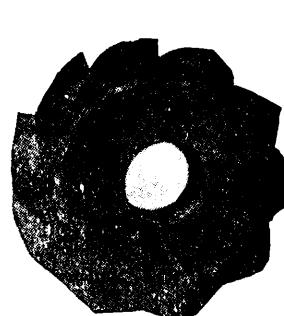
Разрез отливки торцевой фрезы, залитой при низкой температуре металла
